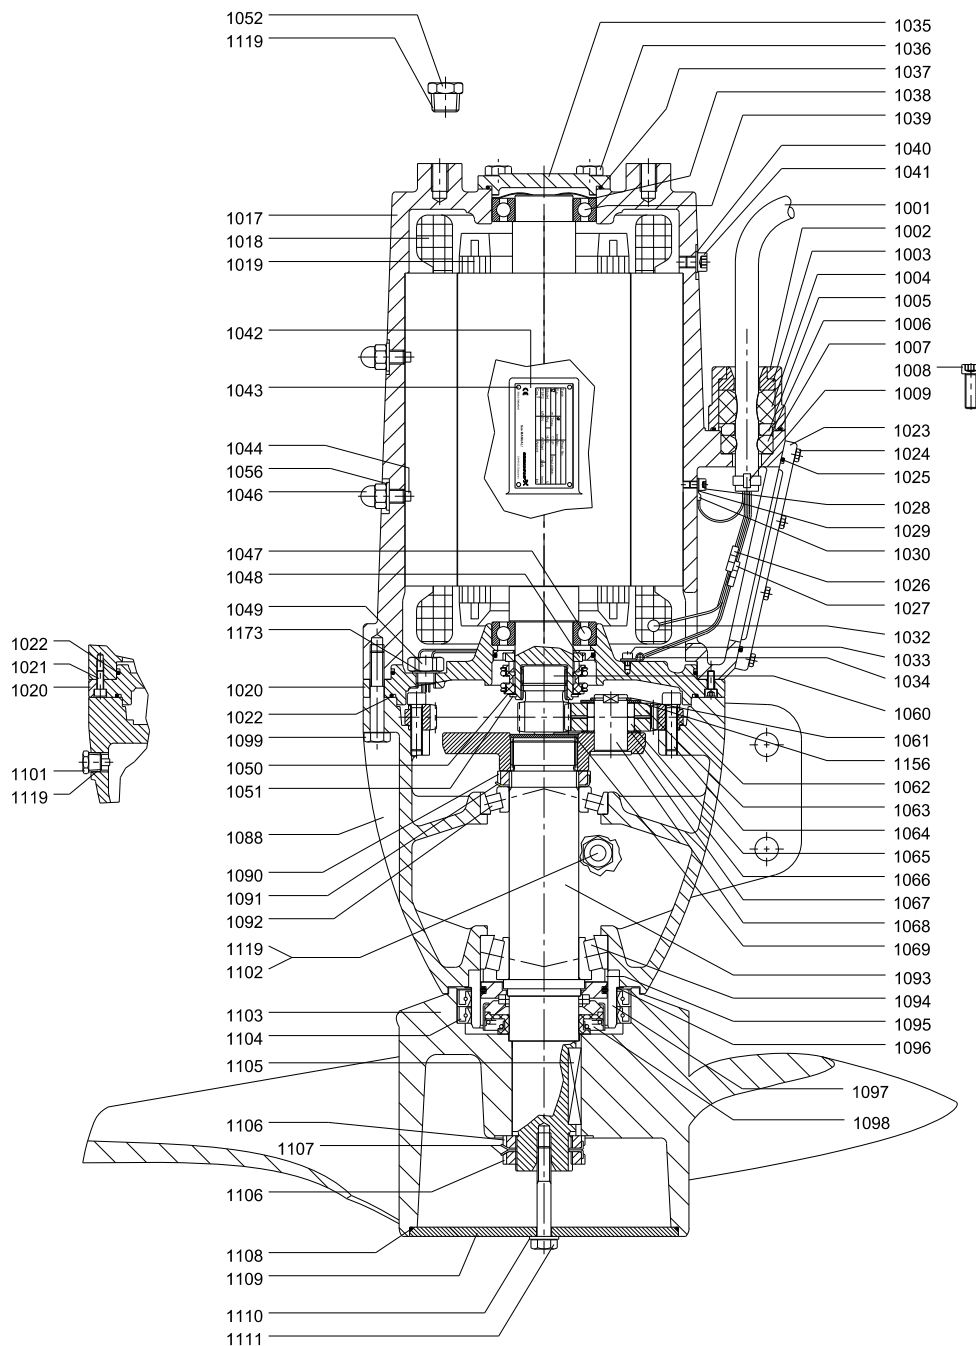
Чертеж в разрезе, SRP.70.80.xxx, SRP.100.80.xxx и SRP.130.80.xxx
